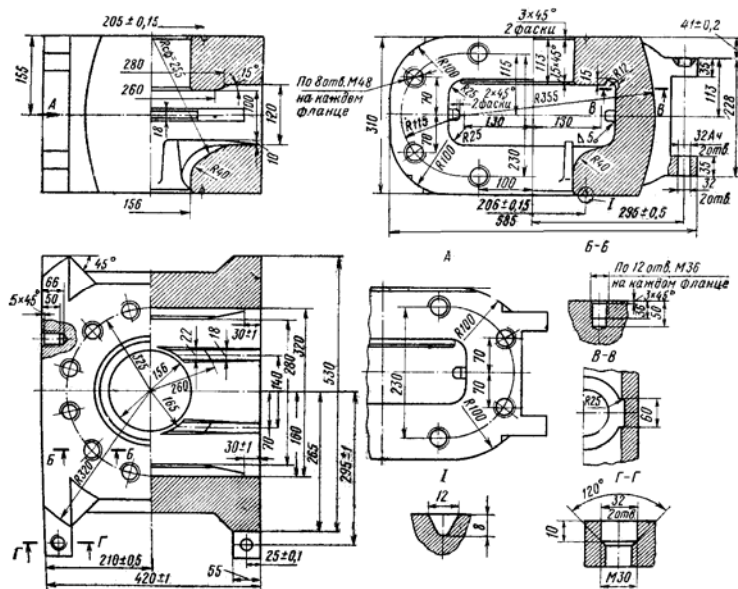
Корпус плашечного превентора ППГ-156×320
